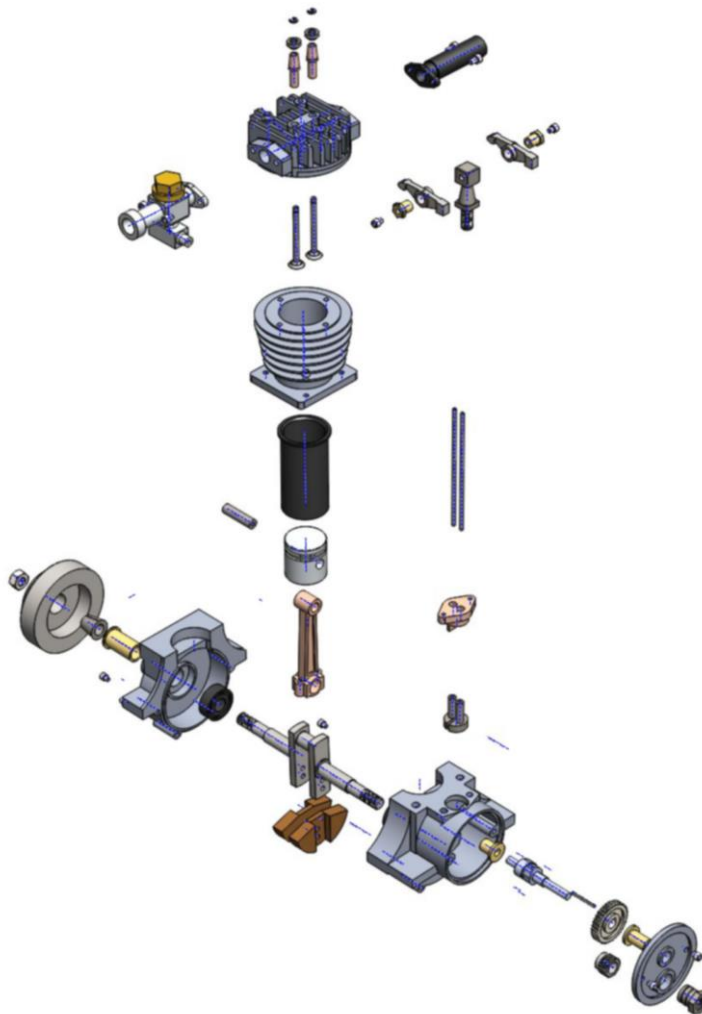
Explosionado de los componentes internos del prototipo de motor de combustión, SolidWorks. [Fuente propia]
